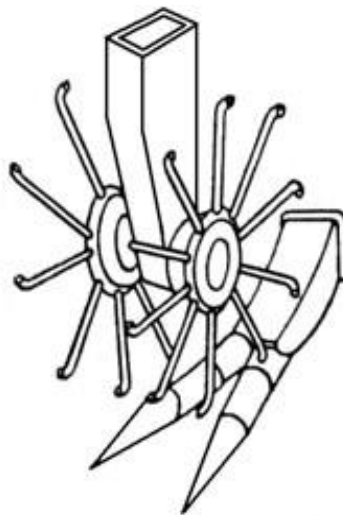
Роторно-вильчастий викопувальний робочий орган
